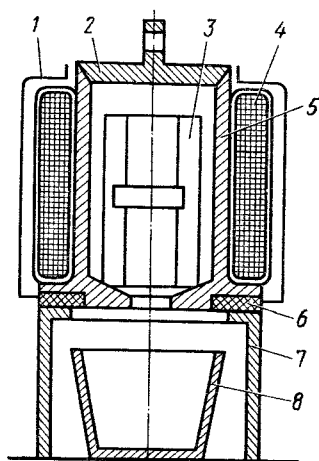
Индукционный нагреватель для выплавки баббита из вкладышей:
